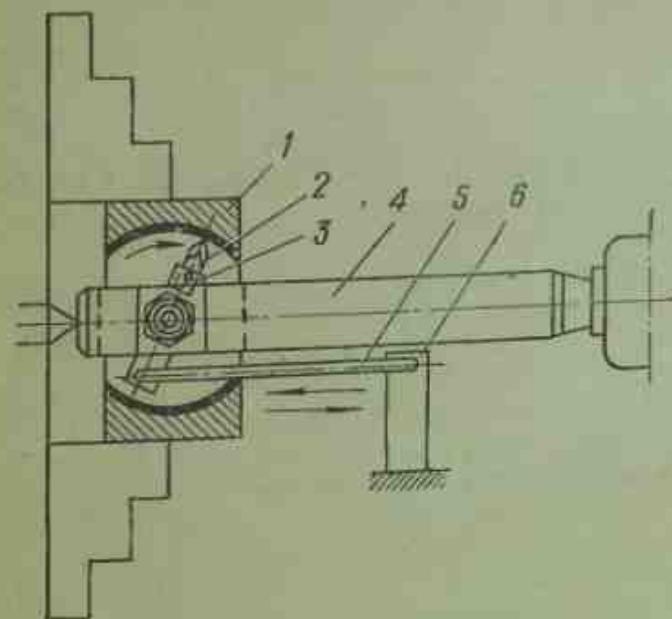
Центровая оправка для растачивания сферической поверхности:
